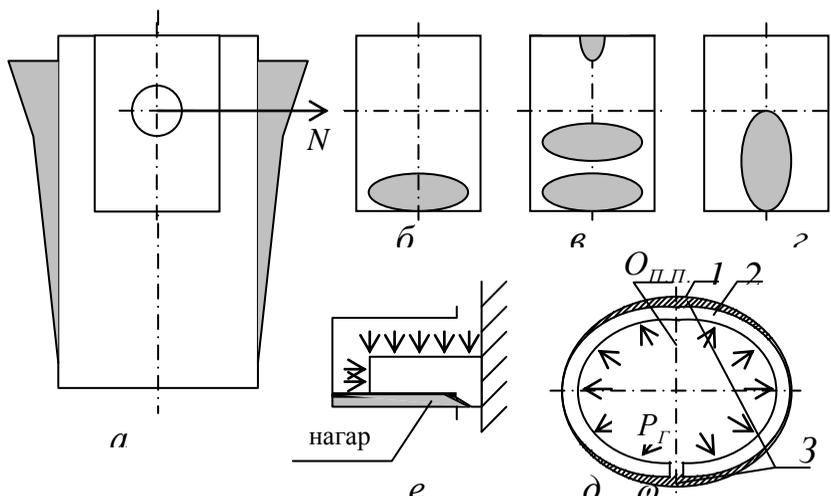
Износ деталей цилиндропоршневой группы:
